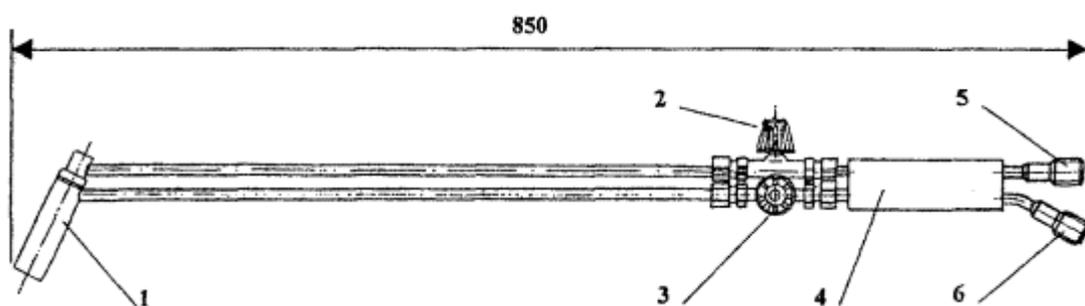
Горелка ПВ-1: 1 - головка горелки; 2 - вентиль подачи воздуха; 3 - вентиль подачи горючего; 4 - державка; 5 - штуцер воздуха М 16×1,5; 6 - штуцер горючего М 16×1,51 Н
